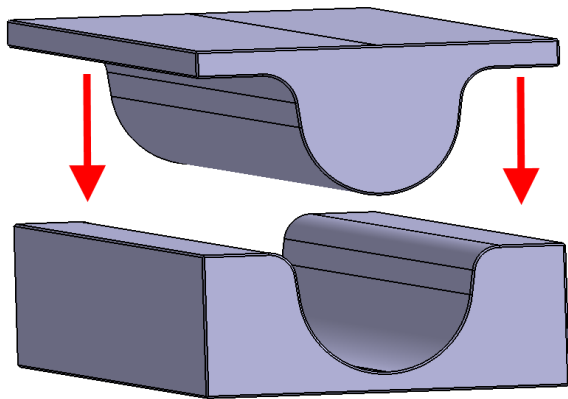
Werkzeug vor Modifikationen aus CAD
